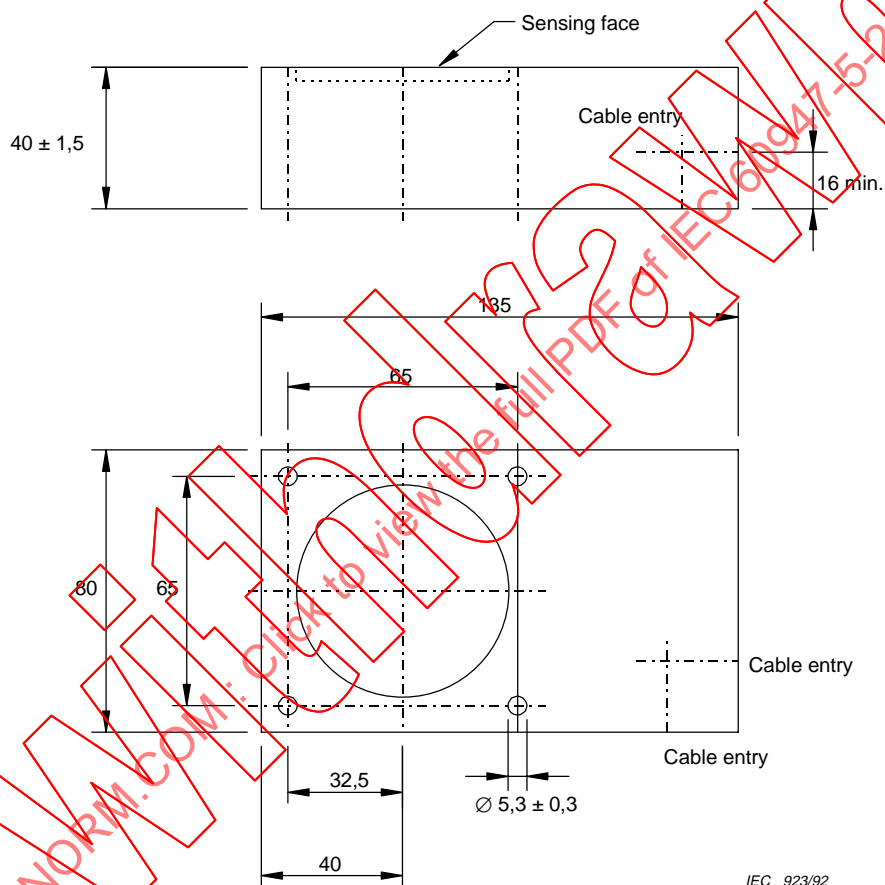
(UD) – Dimensions du type U3D80 en millimètres
